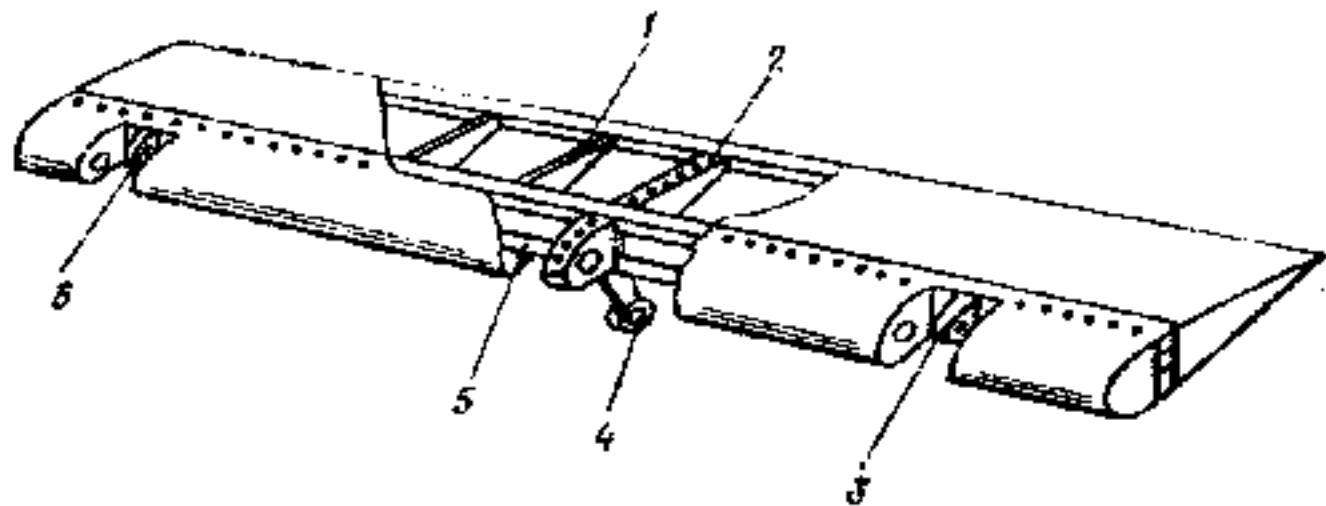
Конструкция элерона с продольным и поперечным силовым набором.
